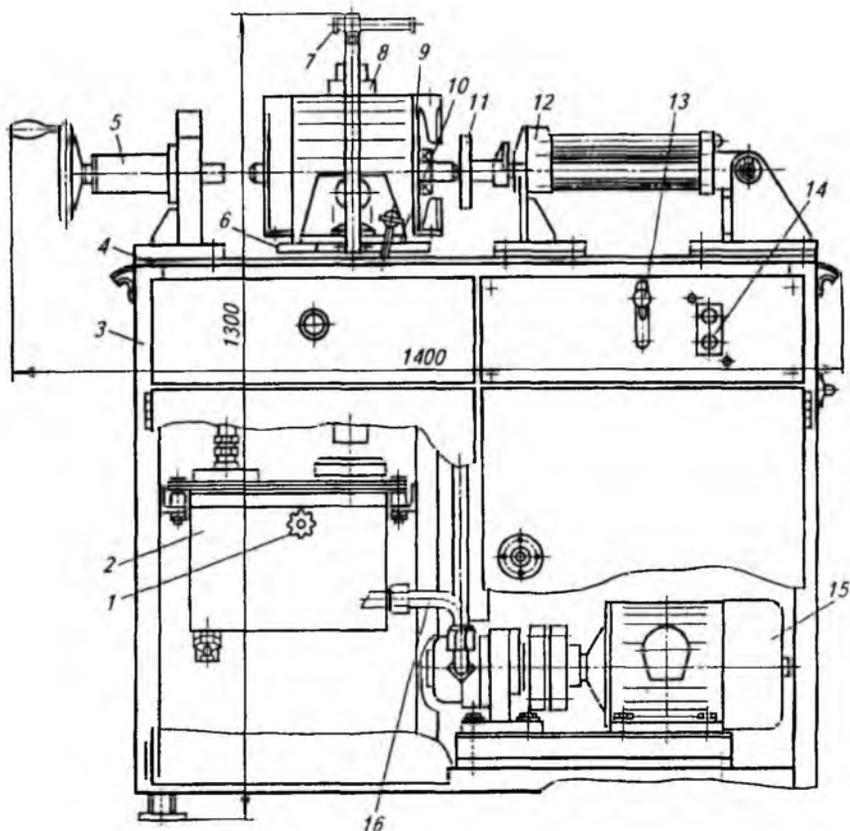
Стенд 8731 для разборки и сборки вакуумных насосов:
